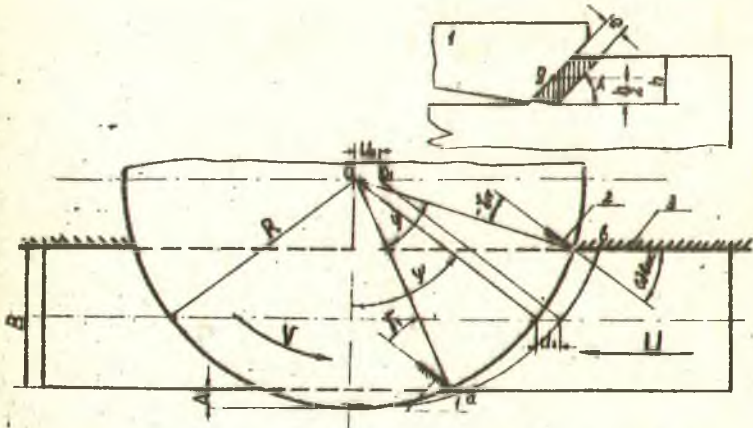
Схема несимметричного встречного торцового фрезерования. 1 - боковой резец, 2 - торцовый резец, 3 - упорная линейка.
